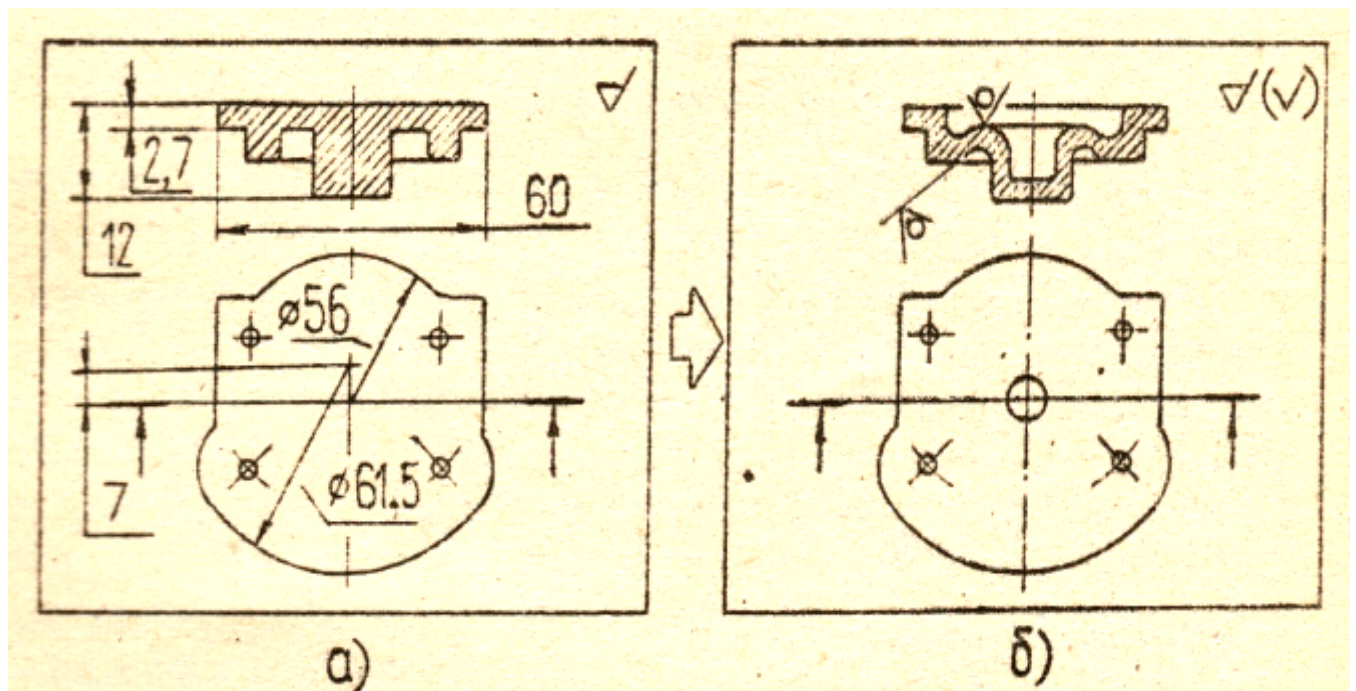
Конструкция крышки держателя (металл — сталь 20)
